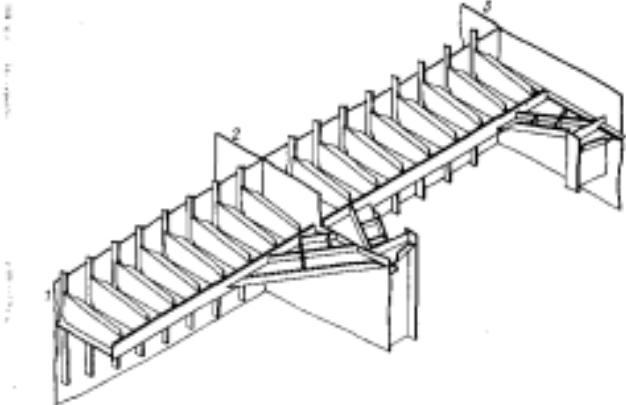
Конструкция шельфа поперечной переборки и его соединение с продольной переборкой и бортом
